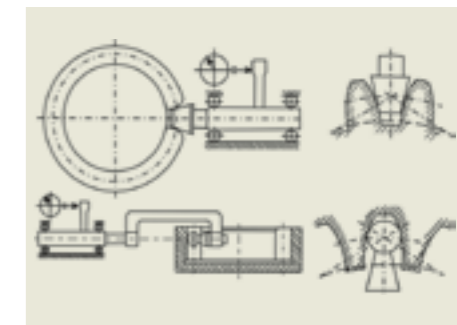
Схема измерения радиального биения зубчатых колес: а – наружного зацепления; б – внутреннего зацепления
